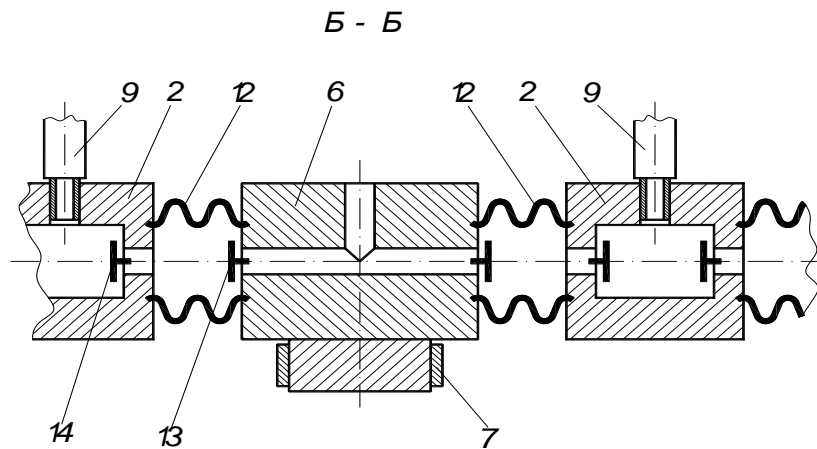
Конструктивна схема віброкомпресора, -- розріз по Б – Б.
